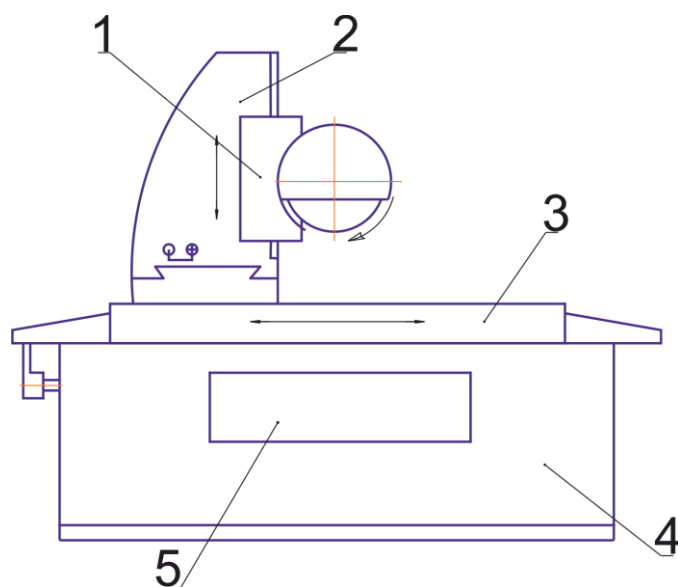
Плоскошліфувальний верстат: 1 – шліфувальна бабка з кругом; 2 - стійка; 3 - стіл; 4 - станина; 5 - привід стола.
